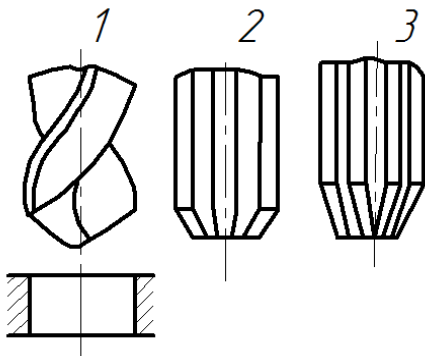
Обробка отвору трьома інструментами за три переходи
